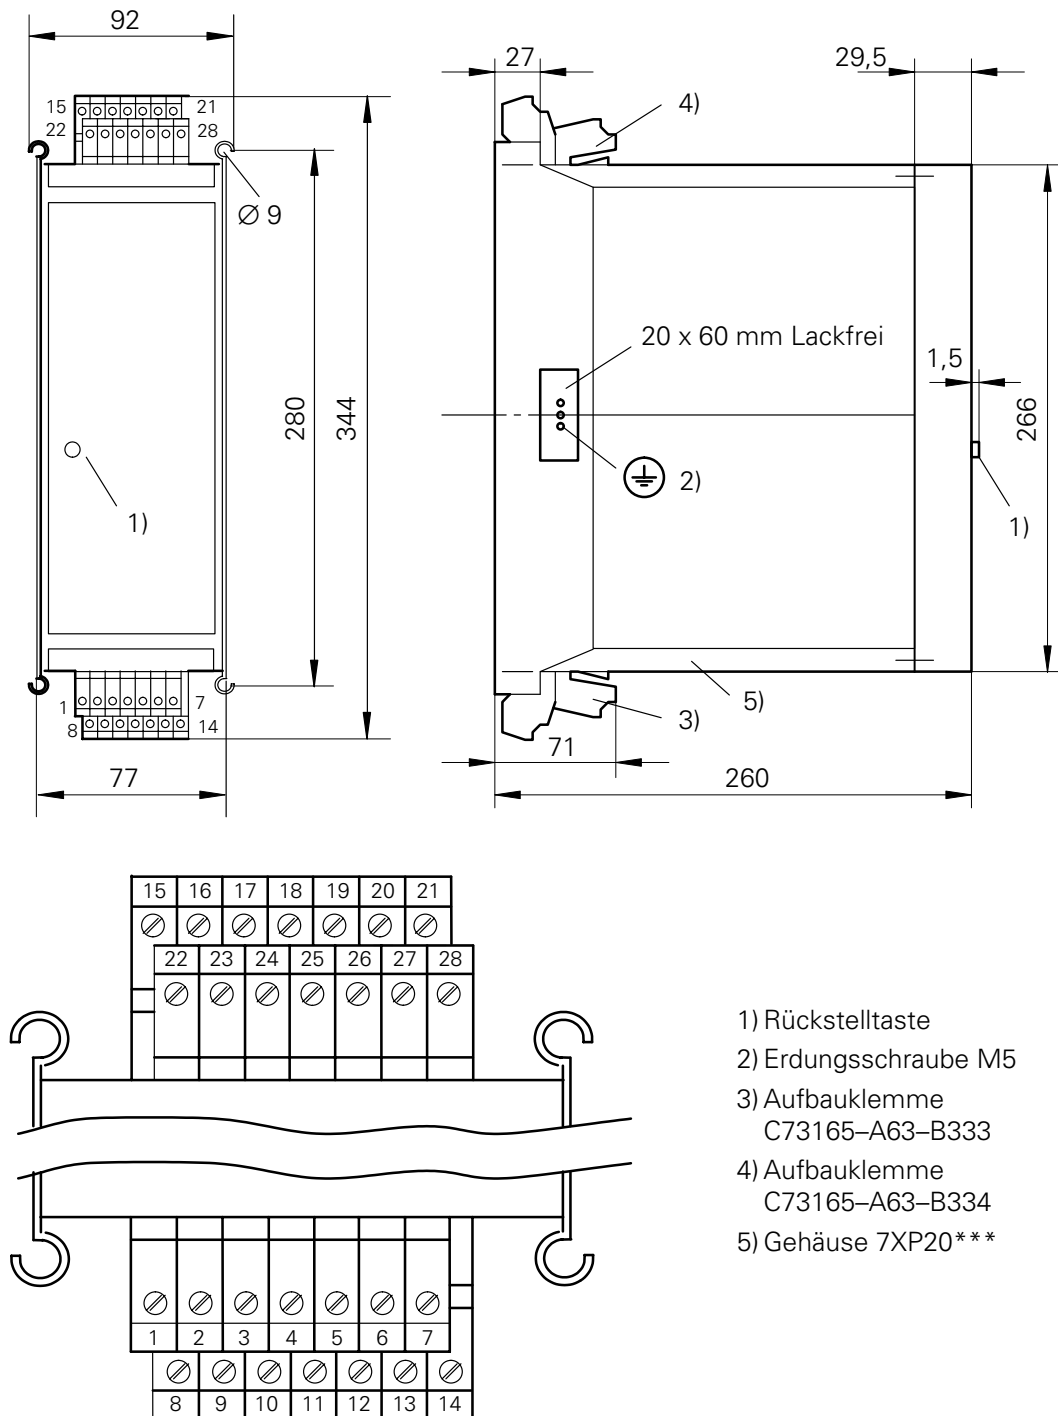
Gehäuseabmessungen, Montage Maße und Klemmenanordnung für Gehäuseausführung Schalttafel Aufbau
